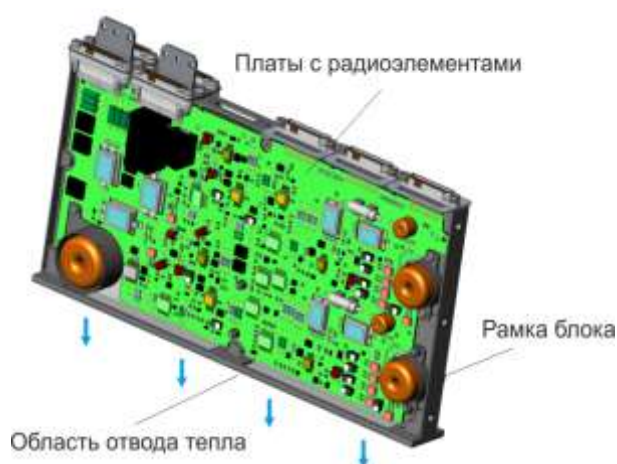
Внешний вид блока бортовой аппаратуры
